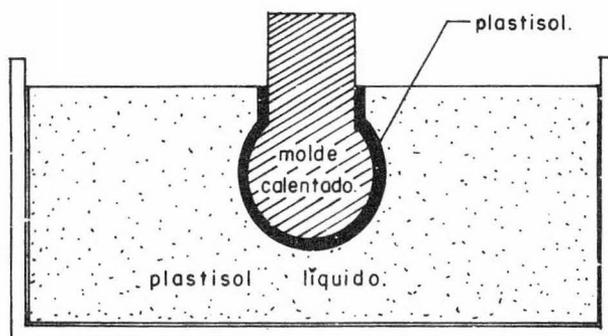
FUNDICION POR INMERSION DE PLASTISOL.
